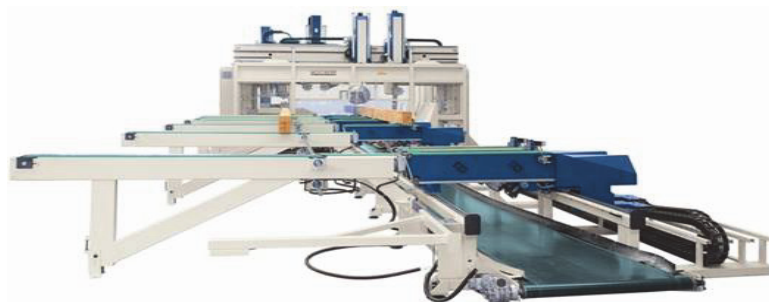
Обрабатывающий ULTRA C13/1.4-BH
